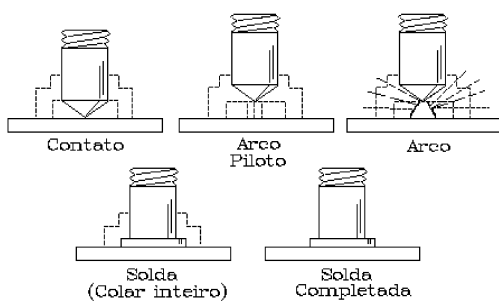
Soldagem a Arco por Prisioneiro.
